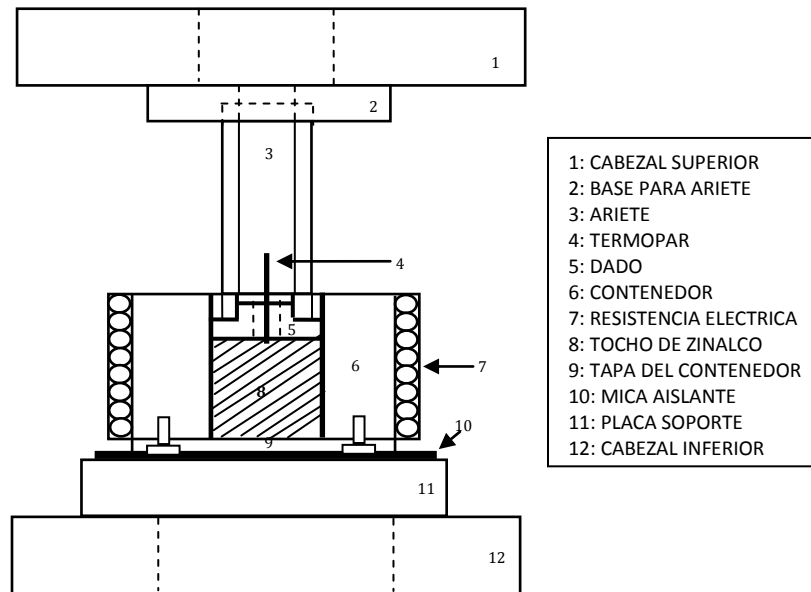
Esquema del dispositivo utilizado para la extrusión inversa de los tochos de Zinalco.
